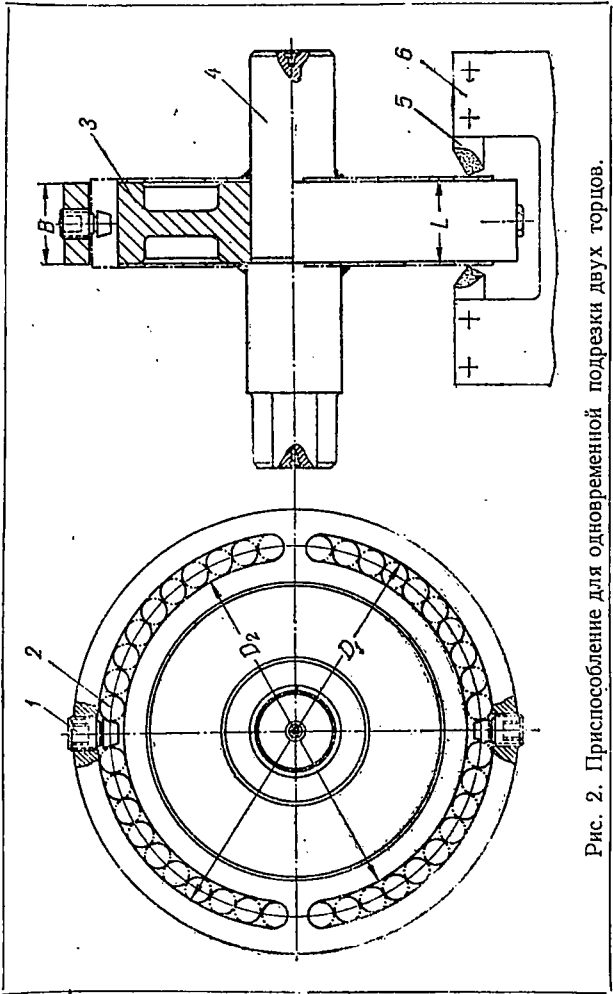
Приспособление для одновременной подрезки двух торцов.
